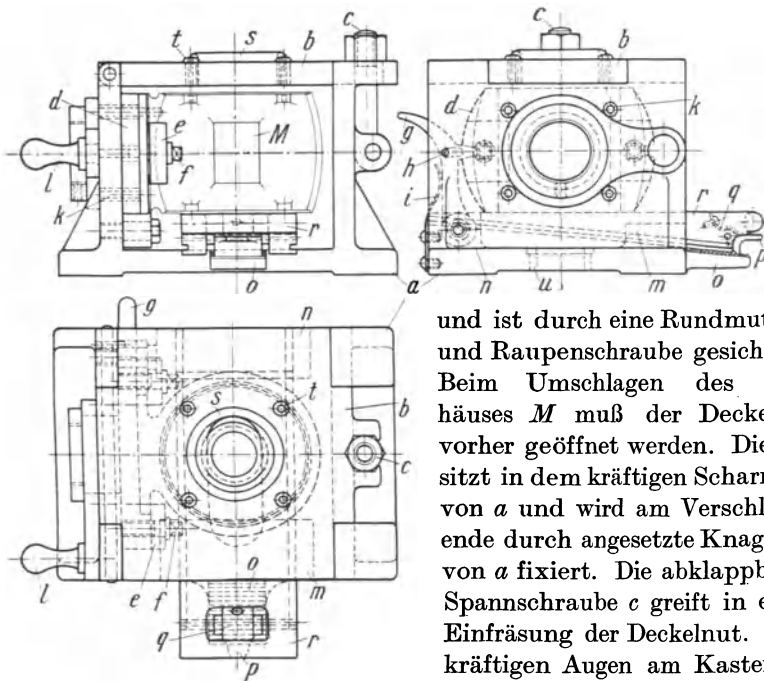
Bohrkasten mit Schwenkvorrichtung für das Bohren an Ventilatormotorgehäusen.
